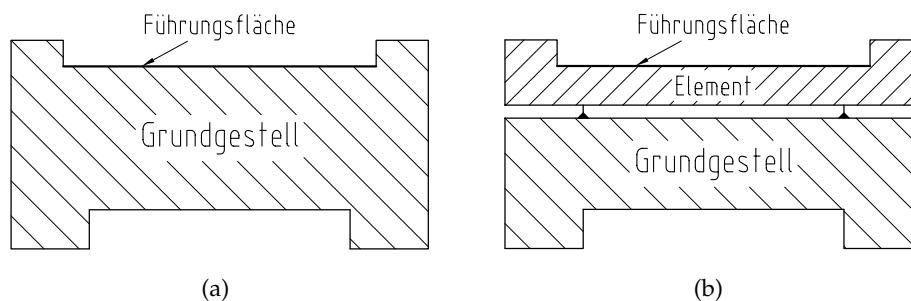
(a) Grundgestell mit integrierten Führungsflächen und (b) Grundgestell mit gesondertem Element für Führungsflächen
